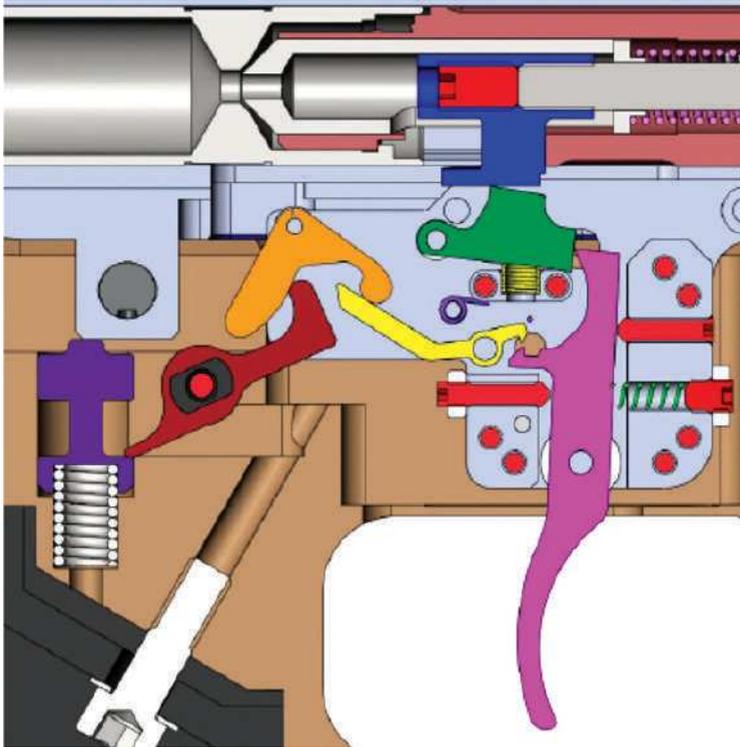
Положення деталей ударно-спускового механізму і затвора після пострілу
